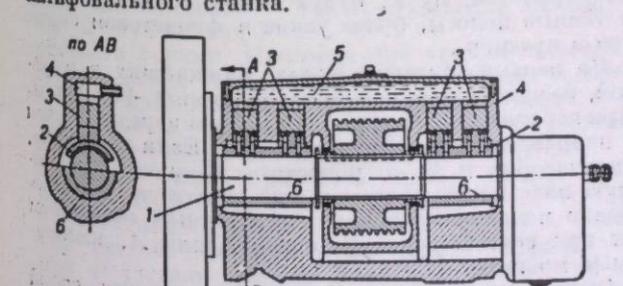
Самоустанавливающийся гидравлический подшипник, непрерывно действующий подвижной компенсатор: 1 — шпиндель круглошлифовального станка; 2 — верхний вкладыш подшипника; 3 — поршни; 4 — крышка подшипника; 5 — масло; 6 — нижний вкладыш подшипника.
